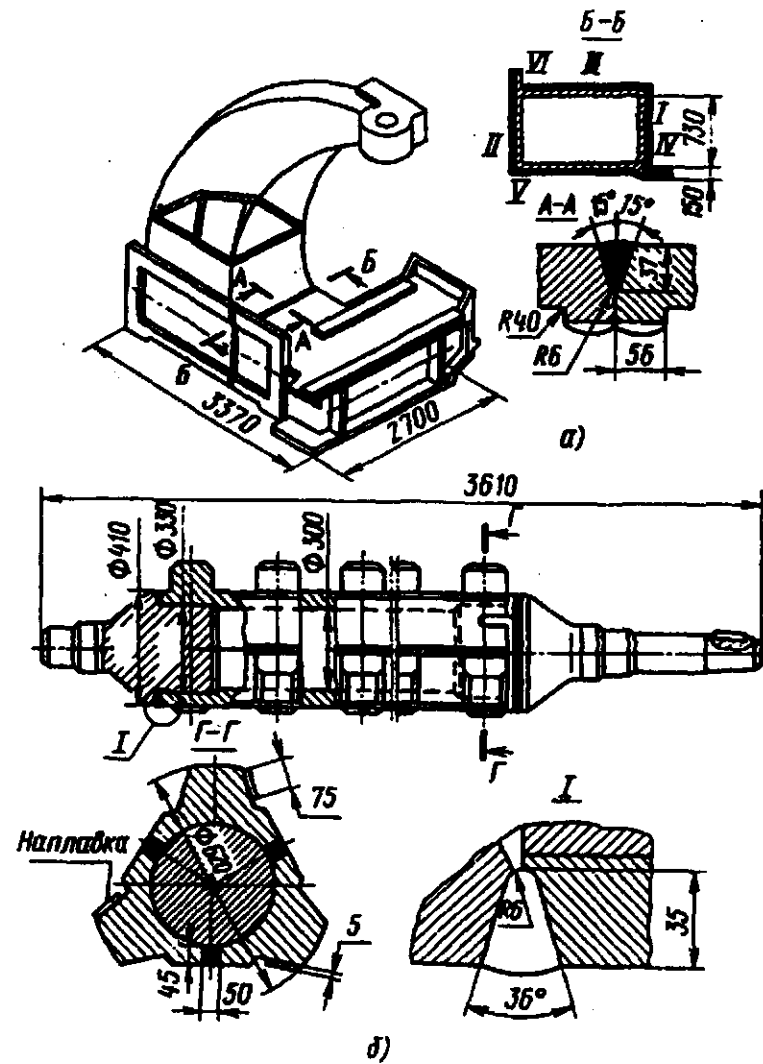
Сварно-литые конструкции: а – ползун; б – вал-звездочка
